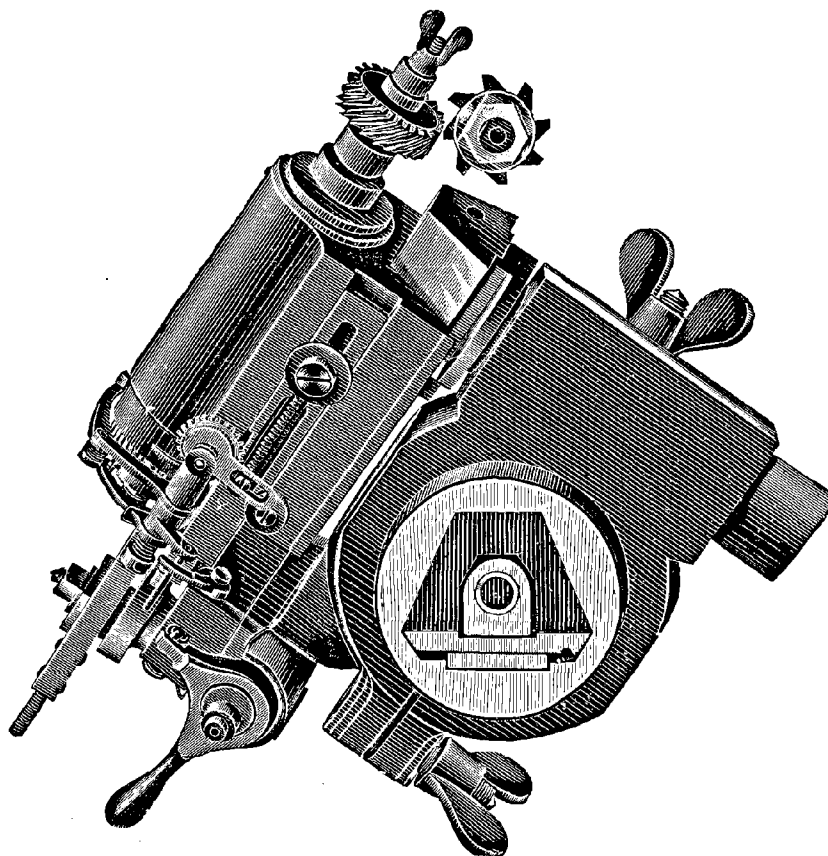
Appareil automatique pour diviser et fraiser les engrenages à dentures hélicoïdales.
